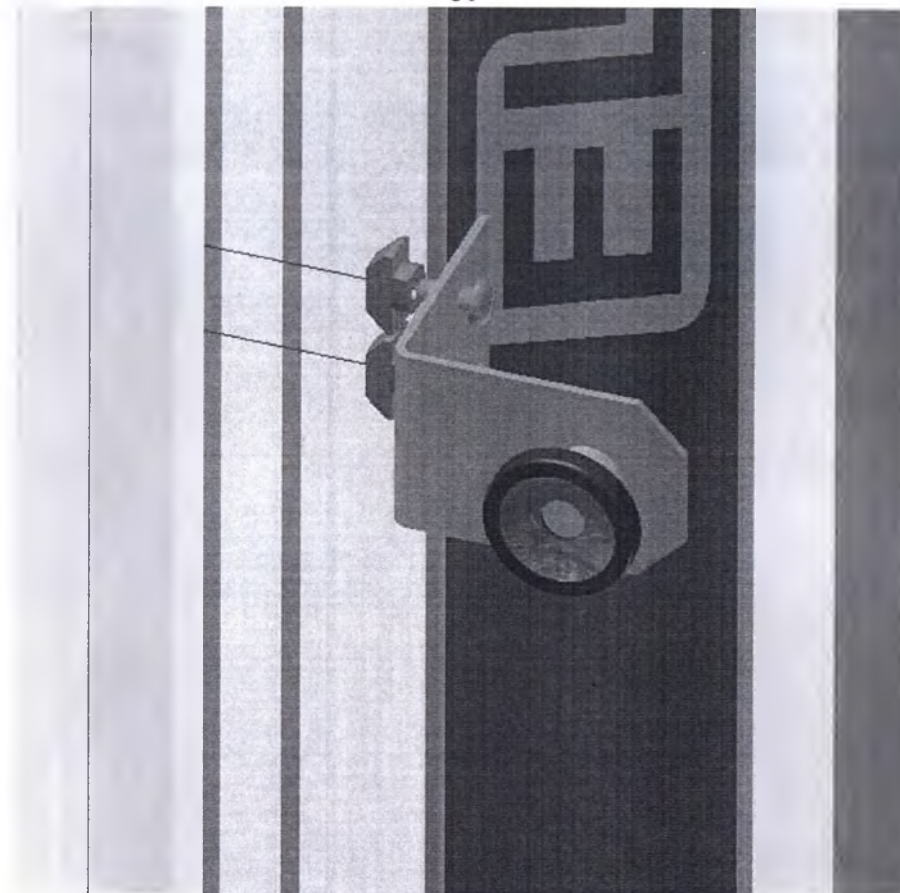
Установка держателя видеоголовки эндоскопической видеокамеры
